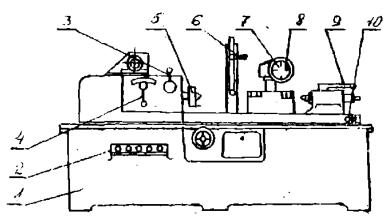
Общий вид станка для шлифования распределительных валов 3A433: I — станина; 2 — пульт кнопочный; 3 — рукоятка отвода люльки; 4 — рукоятка перевода опорного ролика копира; 5 — делительное приспособление; 6 — кран регулировки подачи охлаждающей жидкости; 7 — маховик поперечной подачи шлифовальной бабки; 8 — рукоятка компенсации износа шлифовального круга; 9 — рукоятка отвода пиноли задней бабки; 10 — винт поворота верхнего стола
